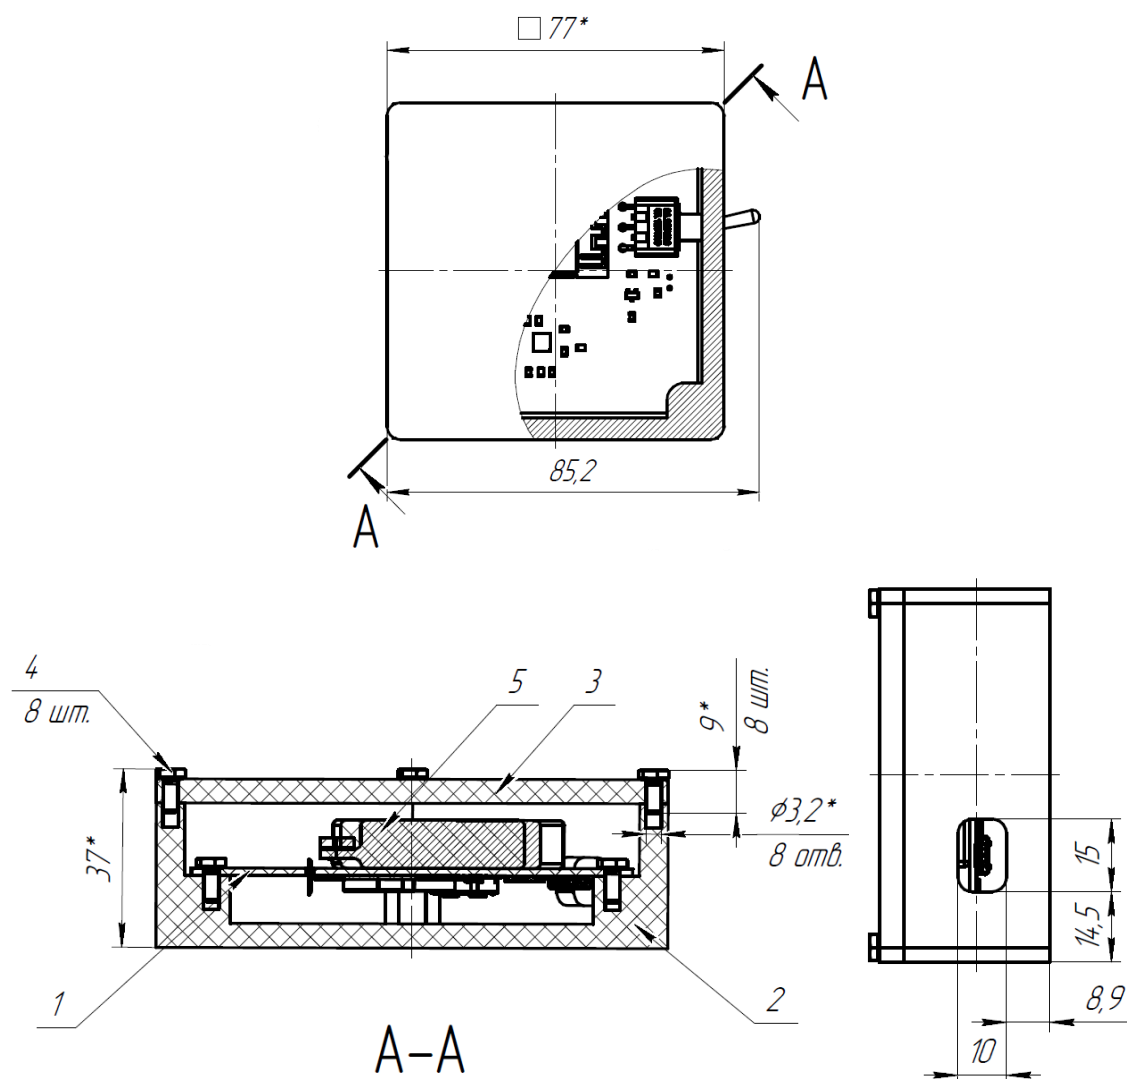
Внешний вид и габаритные размеры корпуса устройства
